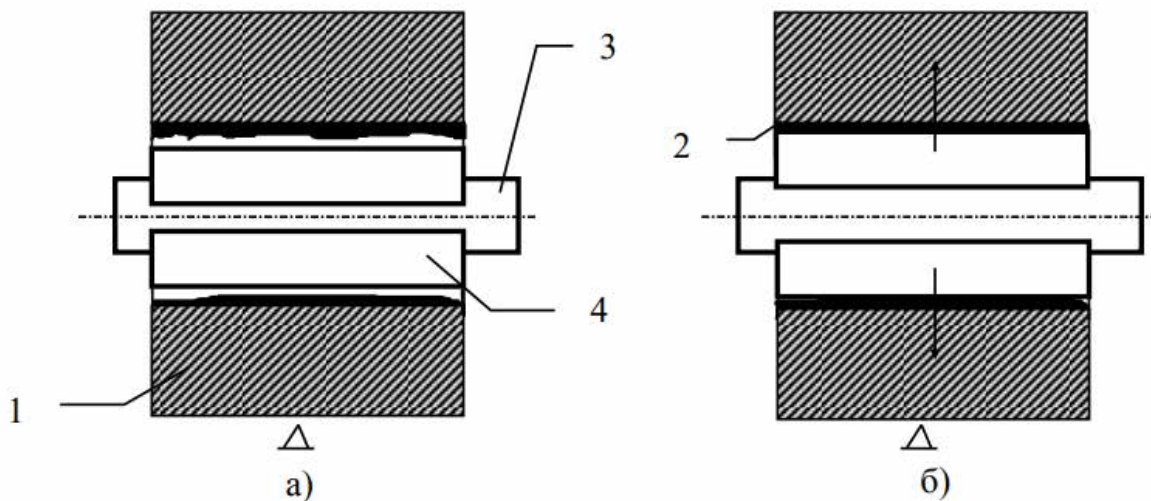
Схема формування полімерної композиції на поверхні зношених отворів корпусних деталей: а) оправлення з кільцями у стислому стані; б) калібрування полімерної композиції кільцями, що розтискаються; 1 – корпусна деталь; 2 – шар полімерної композиції; 3 – оправка; 4 – розсувні півкільця
